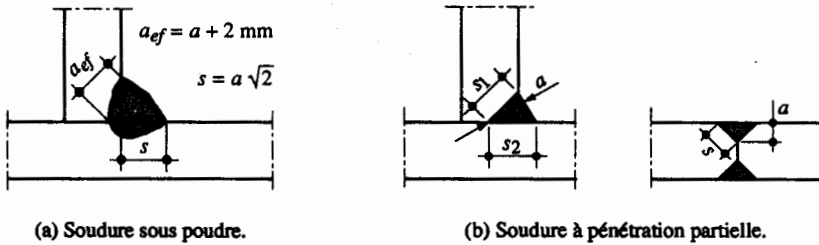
Définition des sections de calcul des soudures sous poudre et à pénétration partielle.
